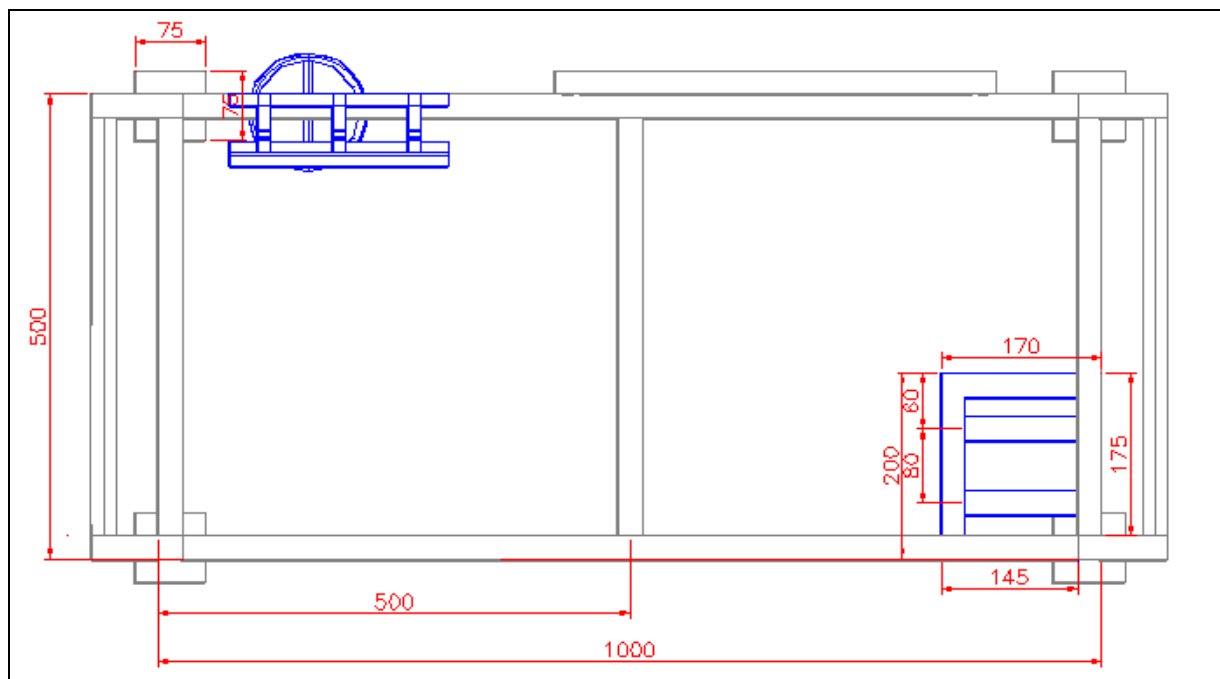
Dimensiones para soporte del motor eléctrico (Fuente: Autor)
